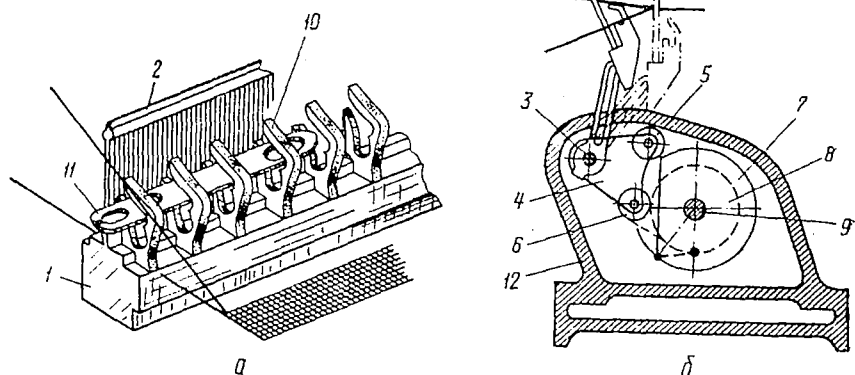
Схема образования ткани (а) и батанный механизм станка СТБ с малогабаритным прокладчиком утка (б)
